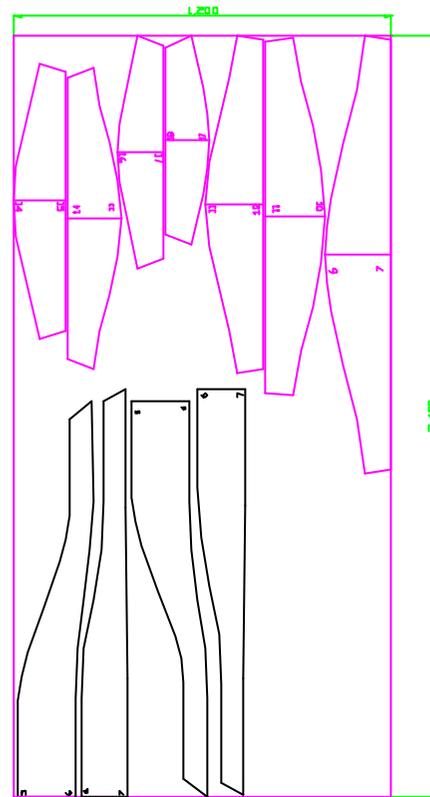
Ubicación de las plantillas del tubo de succión en la plancha de acero para el trazado y oxicorte (Segmentos 5-6 y 6-7; los de la parte superior son segmentos de la espiral)
